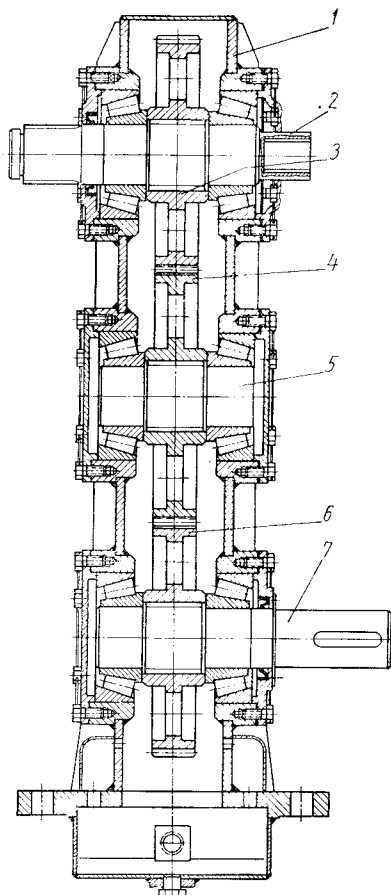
Редуктор привода генератора экскаватора-каналокопателя Д-583:
